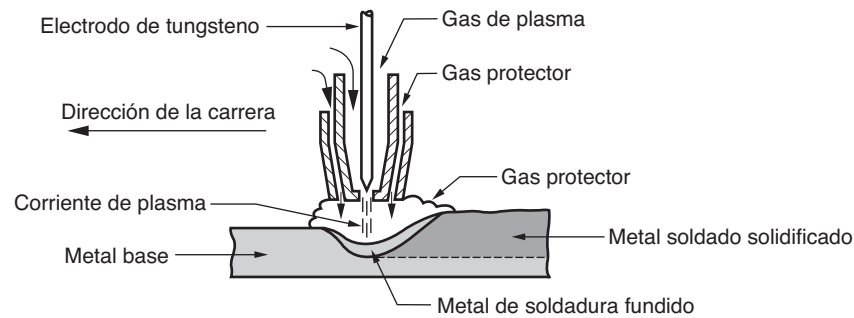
Soldadura con arco de plasma (PAW).
